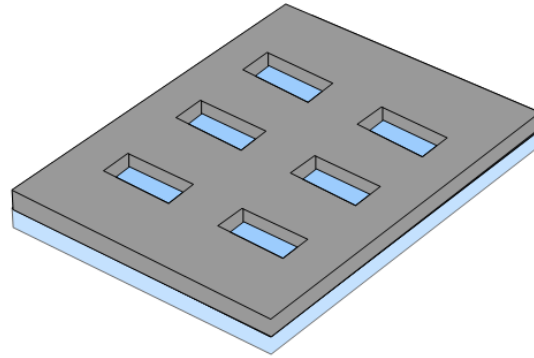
Molde utilizado para la elaboración de placas con dimensiones específicas para cada prueba.
